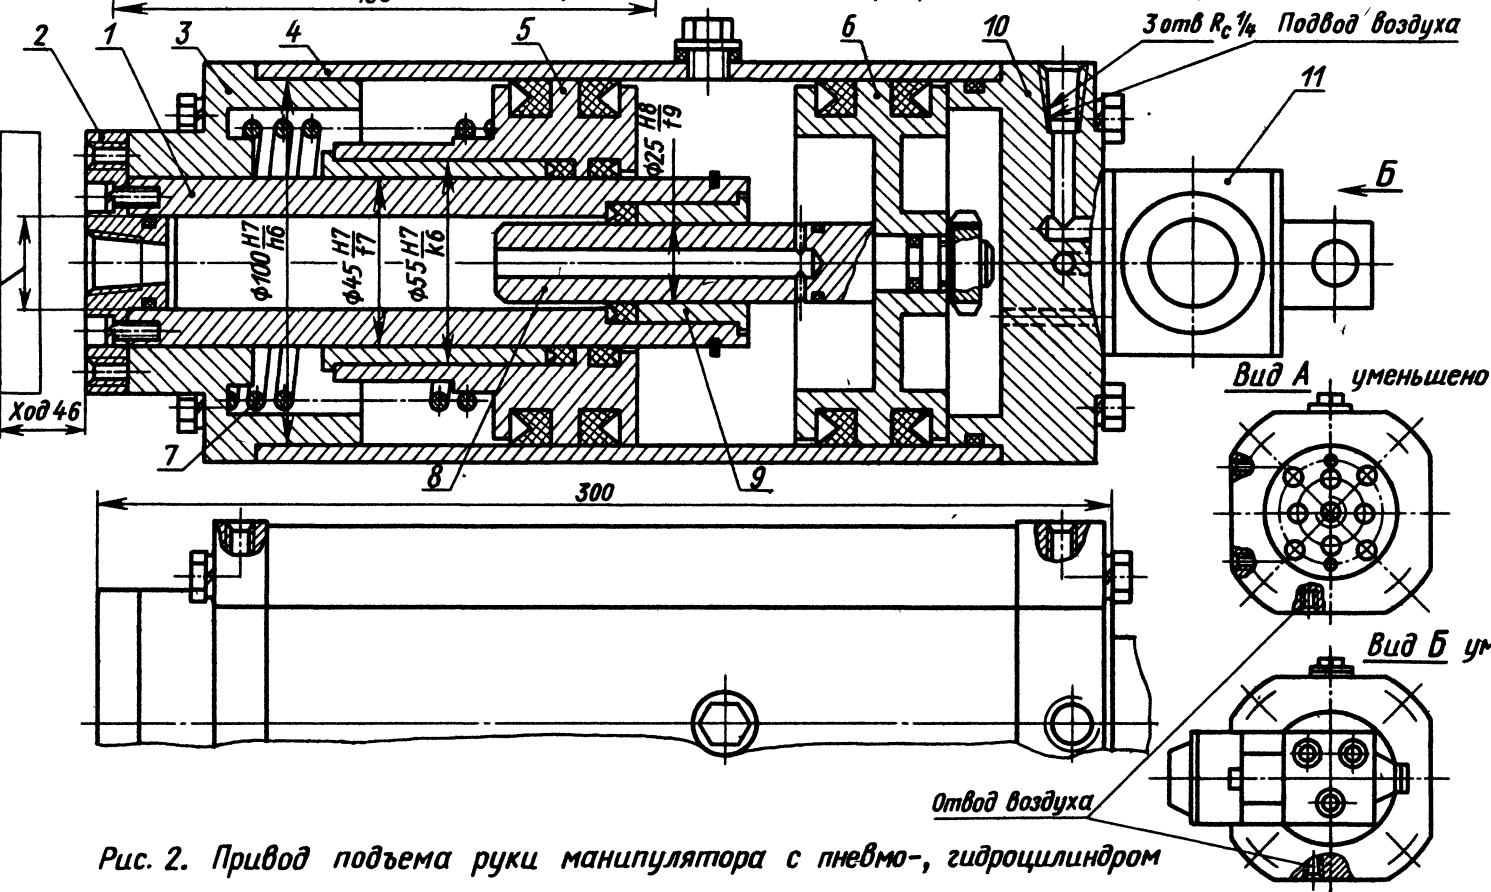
Привод подъема руки манипулятора с пневмо-, гидроцилиндром
